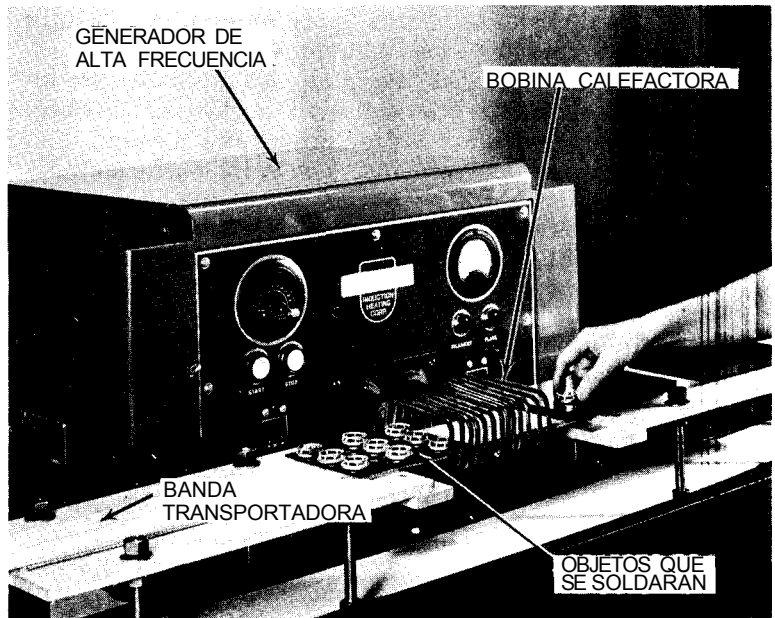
Calefactor por inducción que se emplea para soldadura (Induction Heating Corporation).
